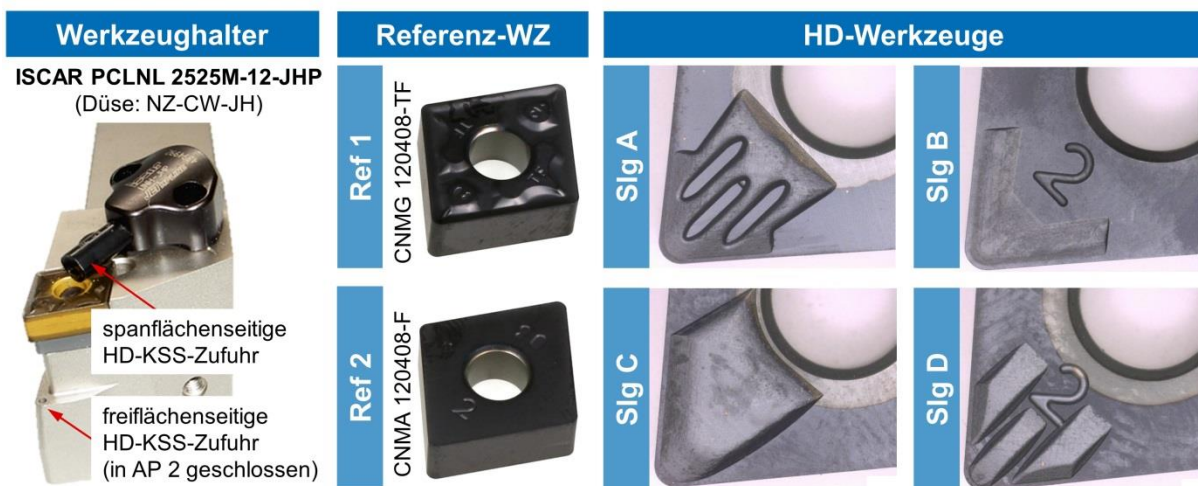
Werkzeughalter und eingesetzte Werkzeuge im Arbeitspaket 2
